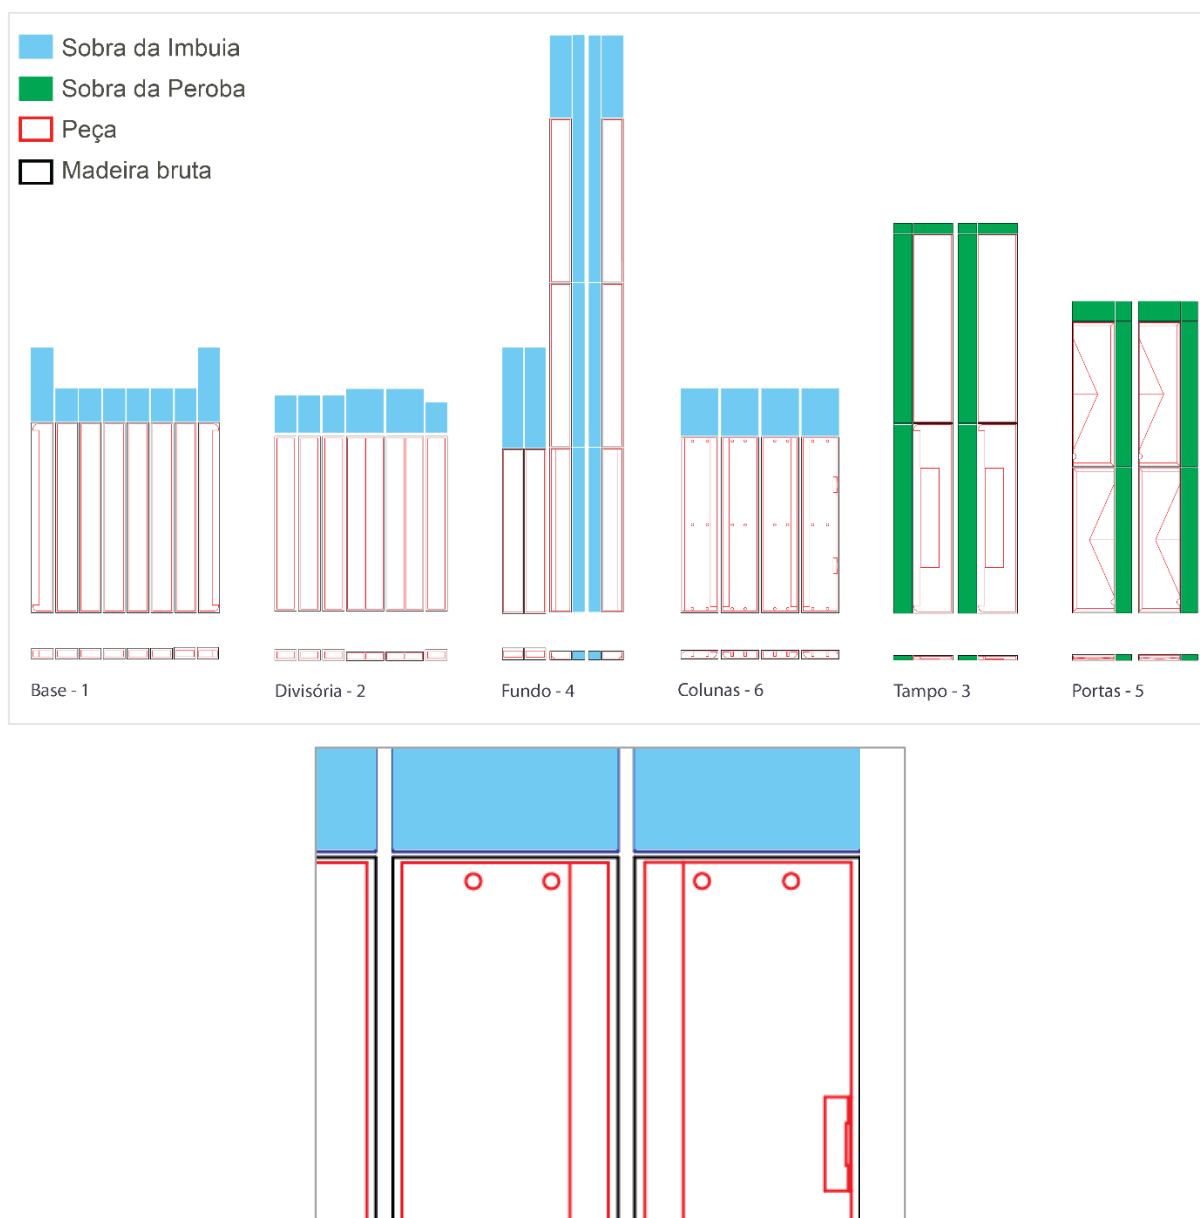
, 114: Plano de corte. Detalhe ampliado do plano de corte do Conjunto-6. Fonte: autor.
